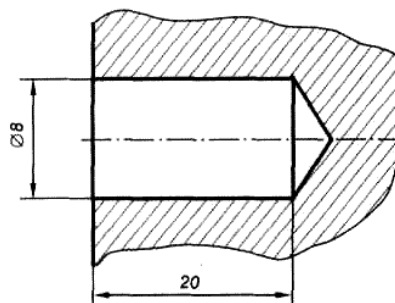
Нанесение размеров отверстия на разрезе детали
